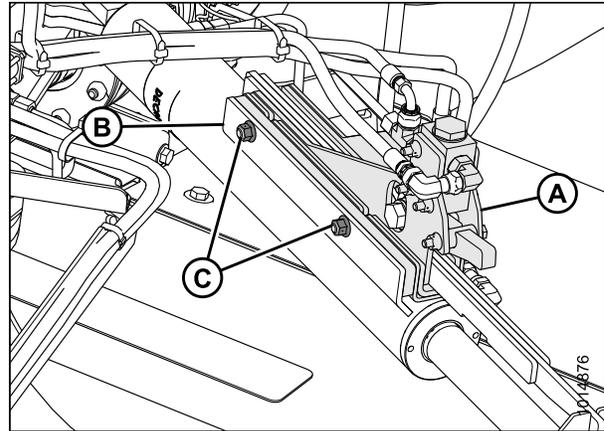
Contrôles d'alignement (vue de l'arrière, à droite)
